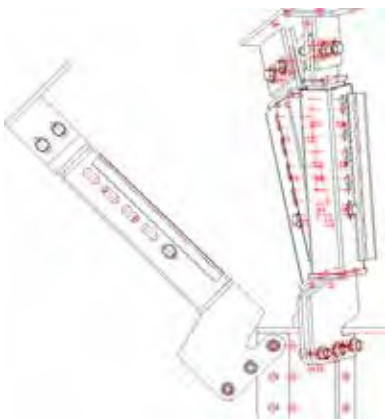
Konstruktion der teleskopierbaren und klappbaren Bühnenkonstruktion
